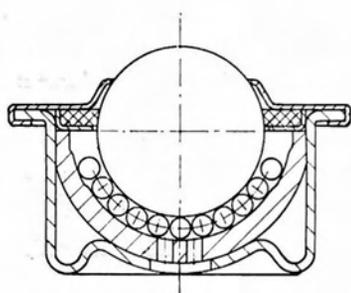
Kugelrolle in blechgepreßtem Gehäuse
